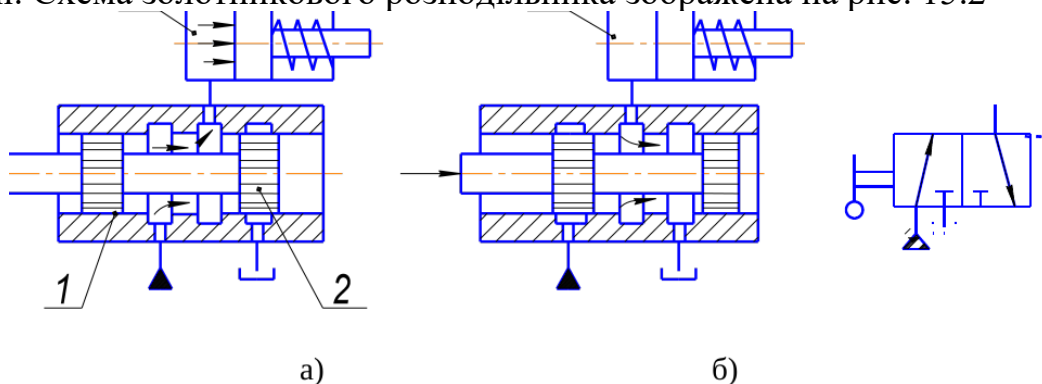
Направляючий розподільник 3/2 з циліндричним золотником: а – подача робочої рідини до гідродвигуна; б – злив; 1 – корпус; 2 – золотник; 3 – гідроциліндр
